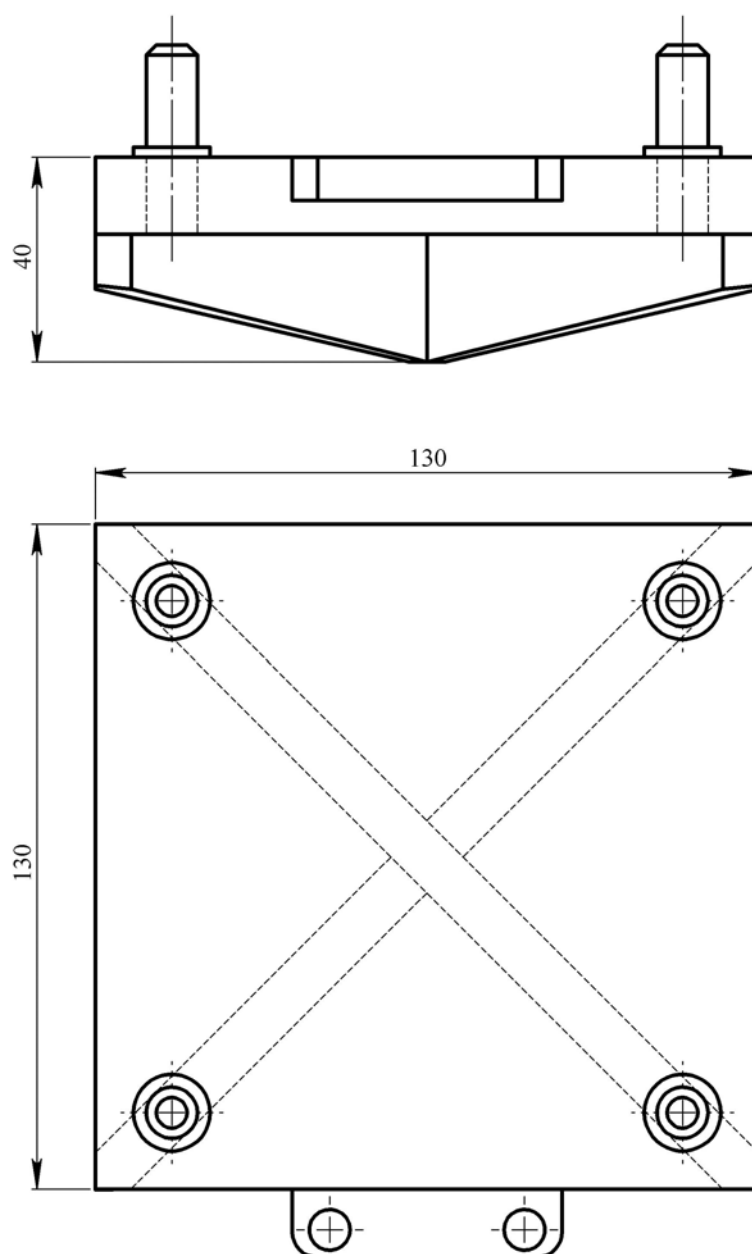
Приспособление для крепления образцов при испытаниях на термостойкость
